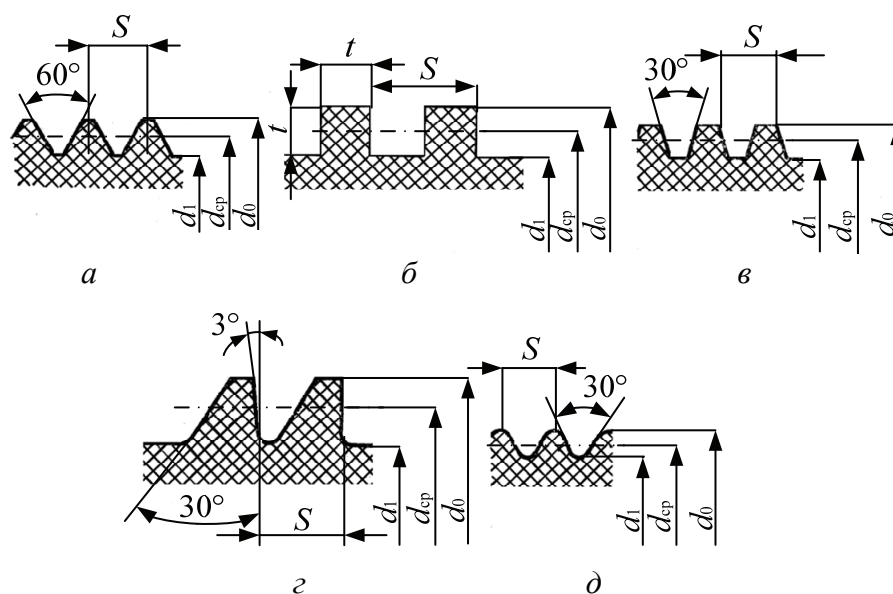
Профили резьбы на пластмассовых изделиях
